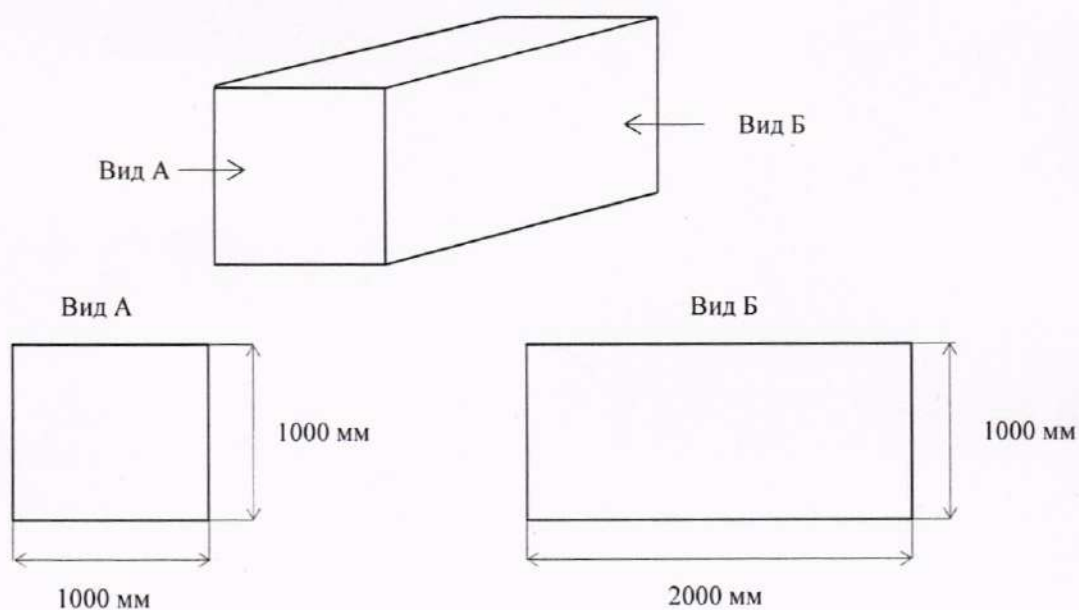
Внешний вид имитатора габаритных размеров № 1
